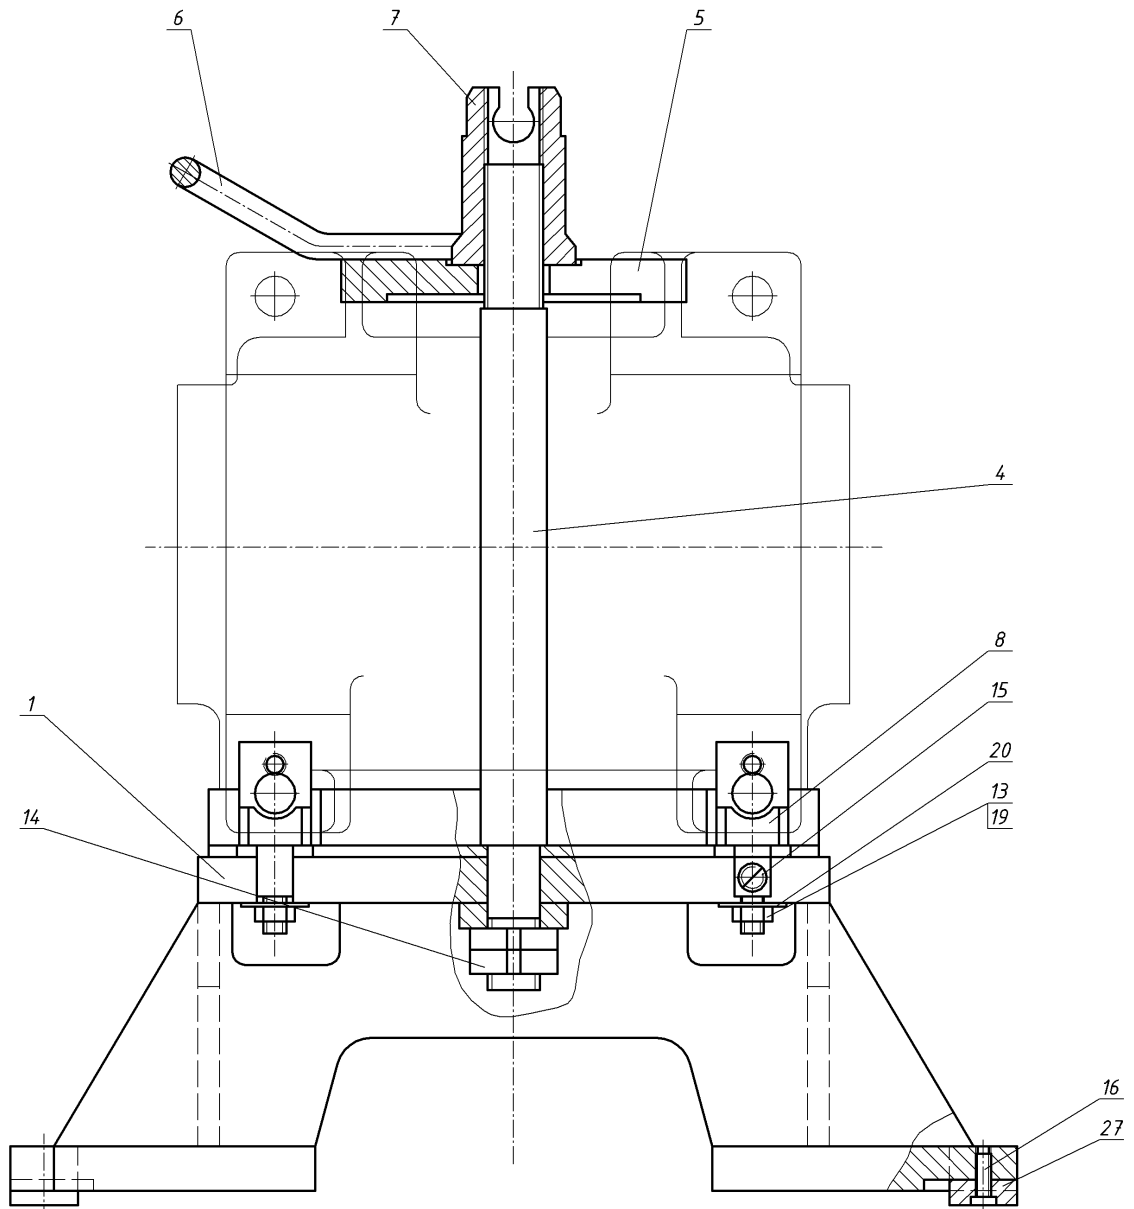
Пристрій для фрезерування та свердління 4-х отворів Ø18
